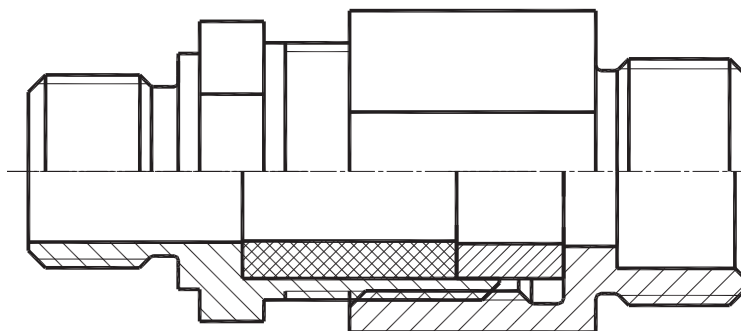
Конструкция ВКВ для монтажа кабеля в трубе.
